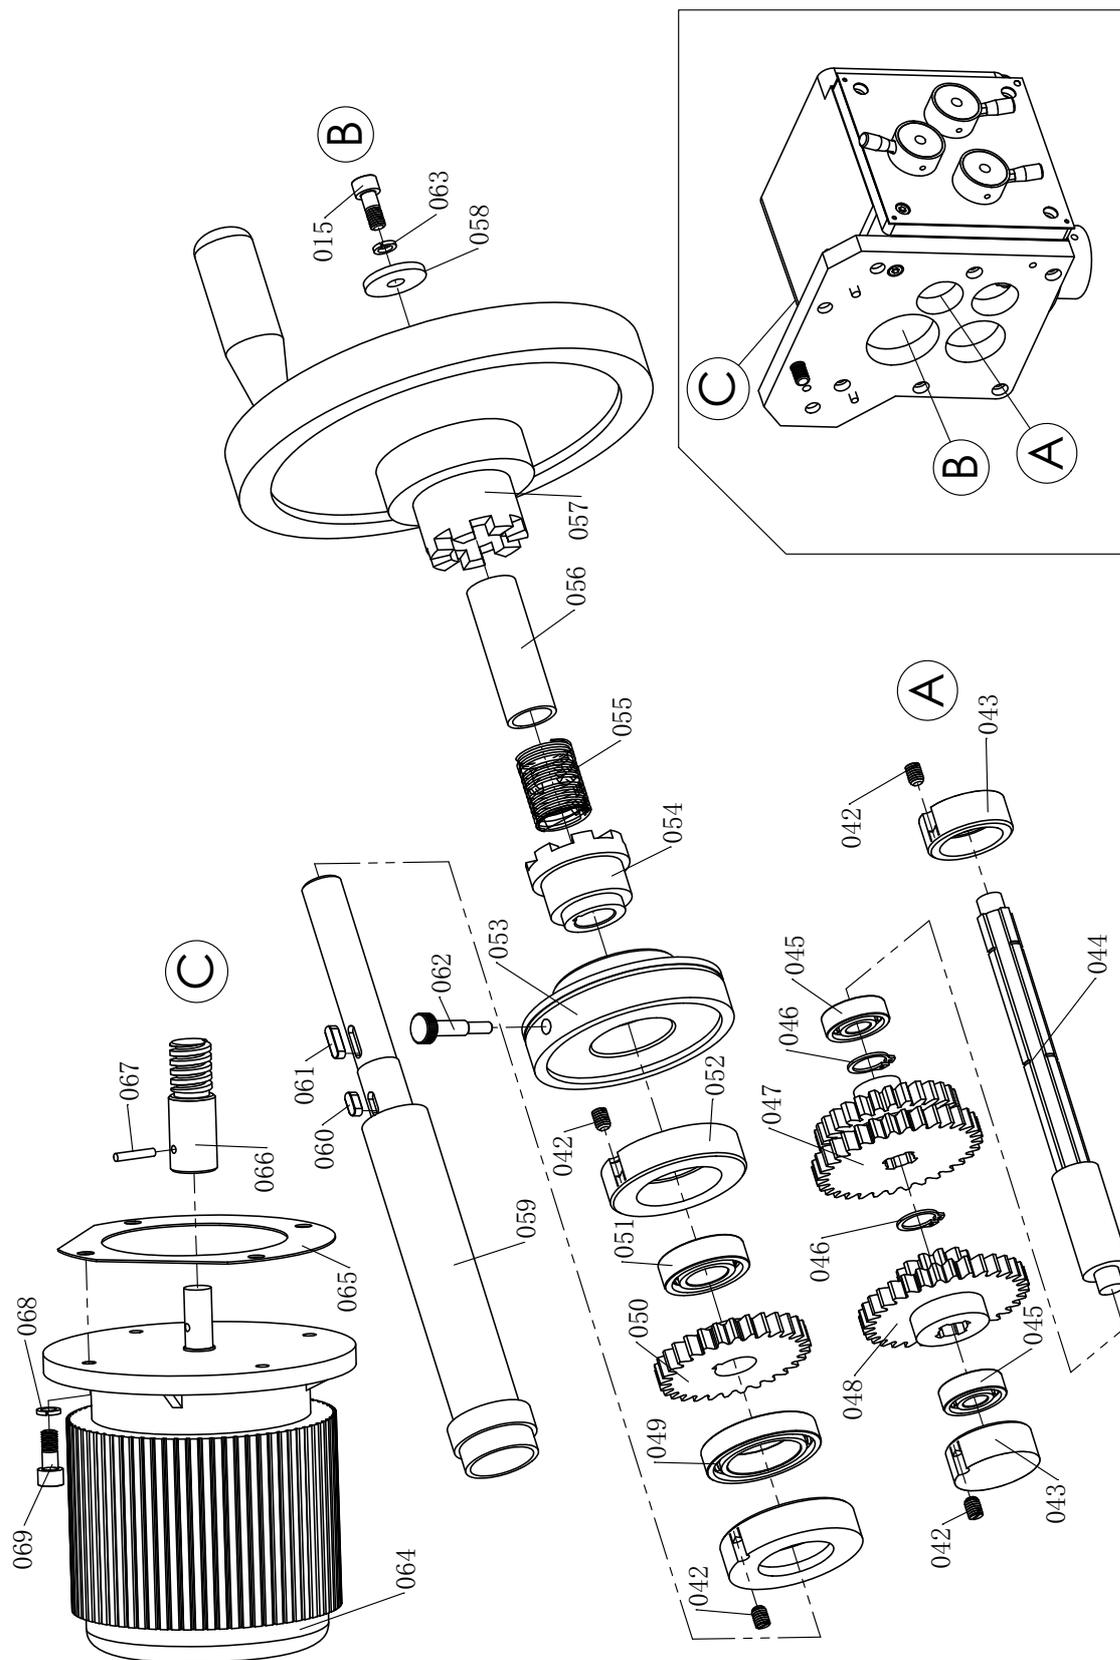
Vorschubgetriebe X-Achse - Feed gear X-Axis 2 - 3
